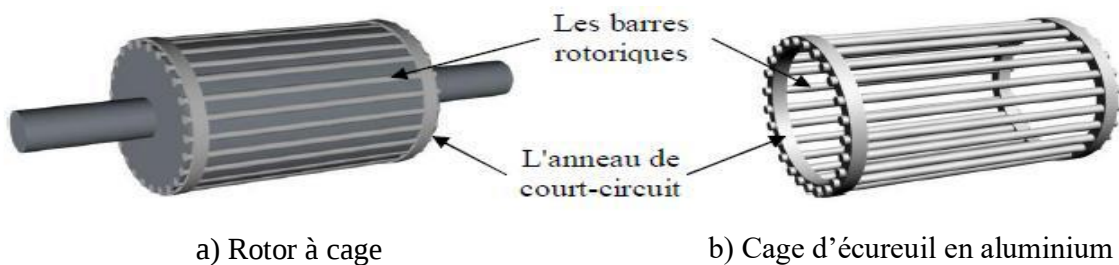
Rotor de la machine asynchrone triphasée à cage
